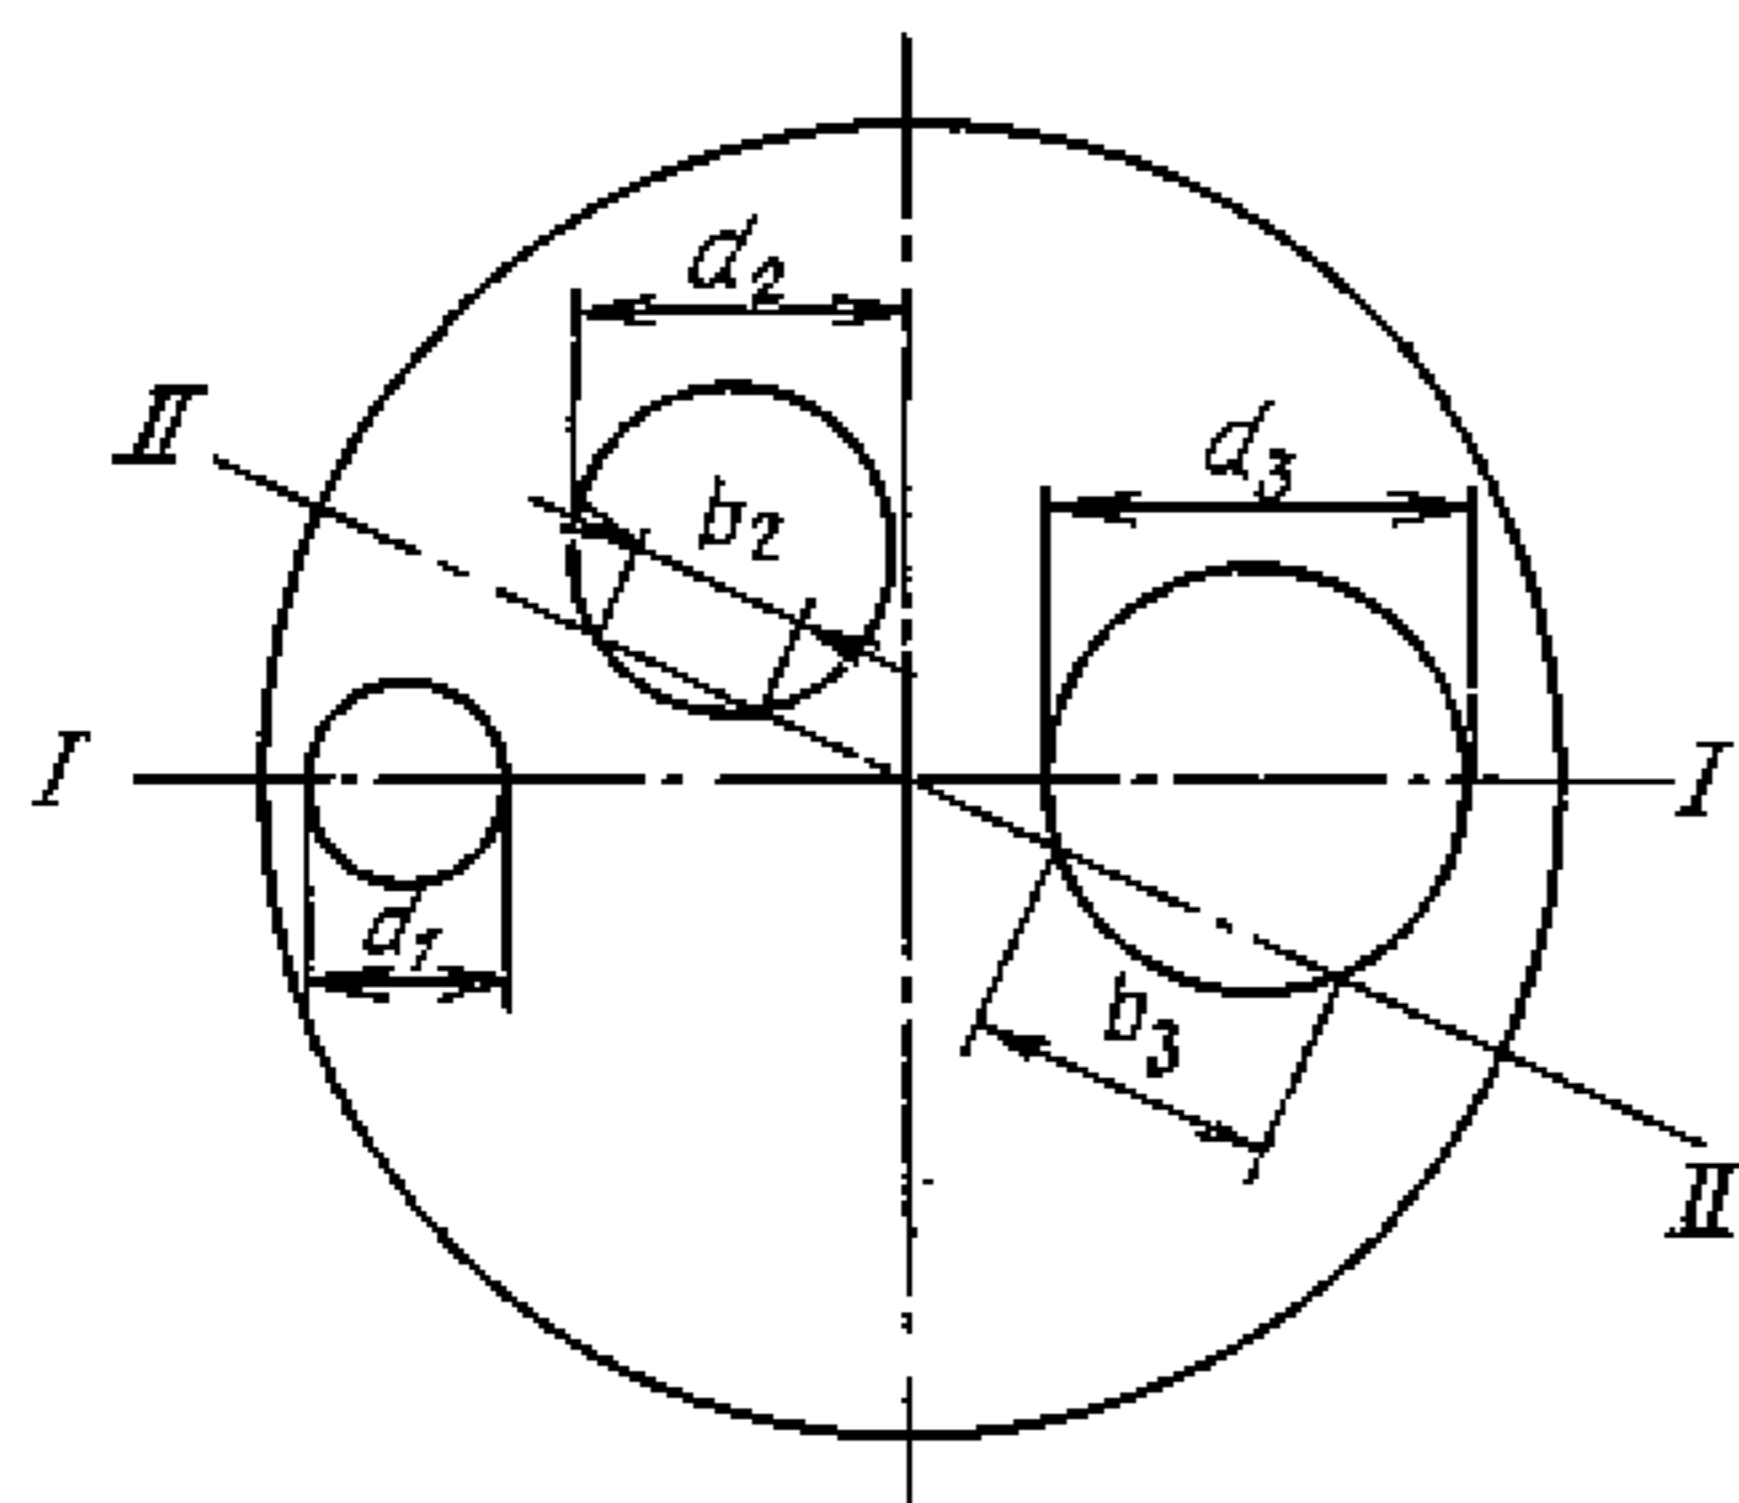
Днище или крышка с неодинаковыми отверстиями и шагами
